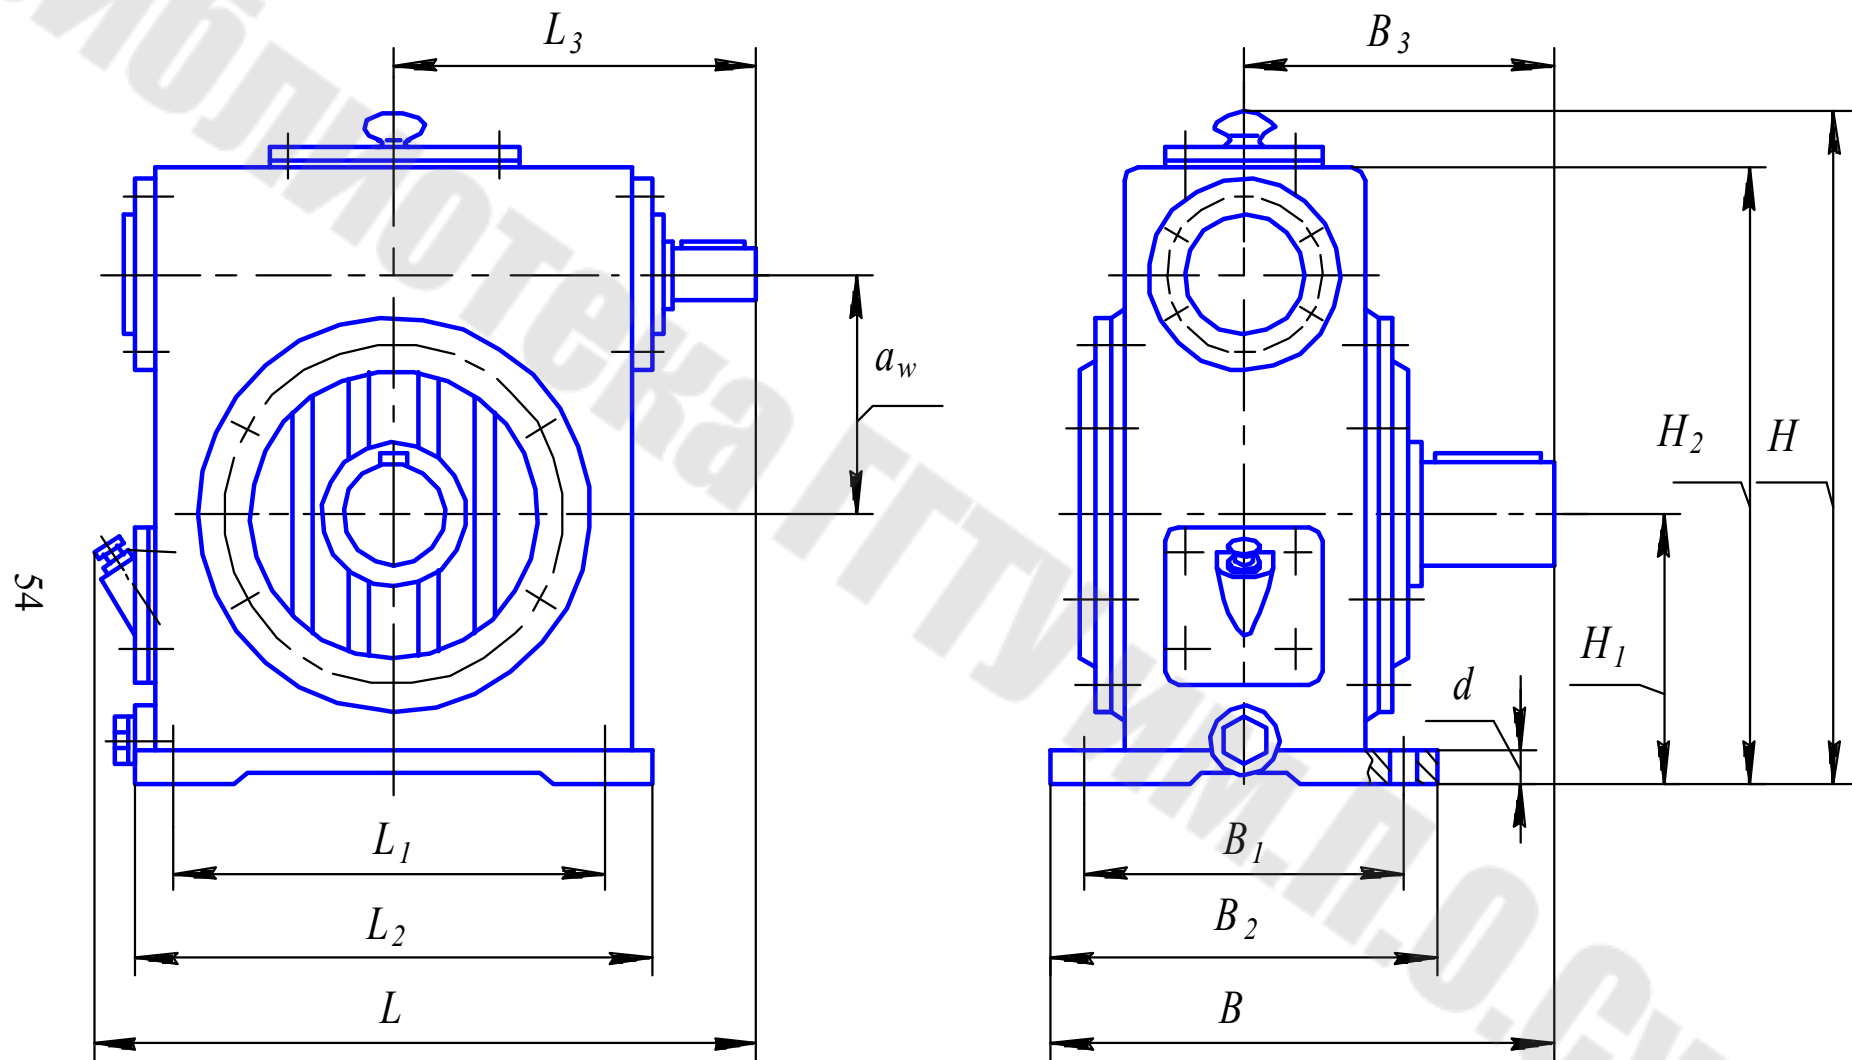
Габаритные и присоединительные размеры червячного редуктора
